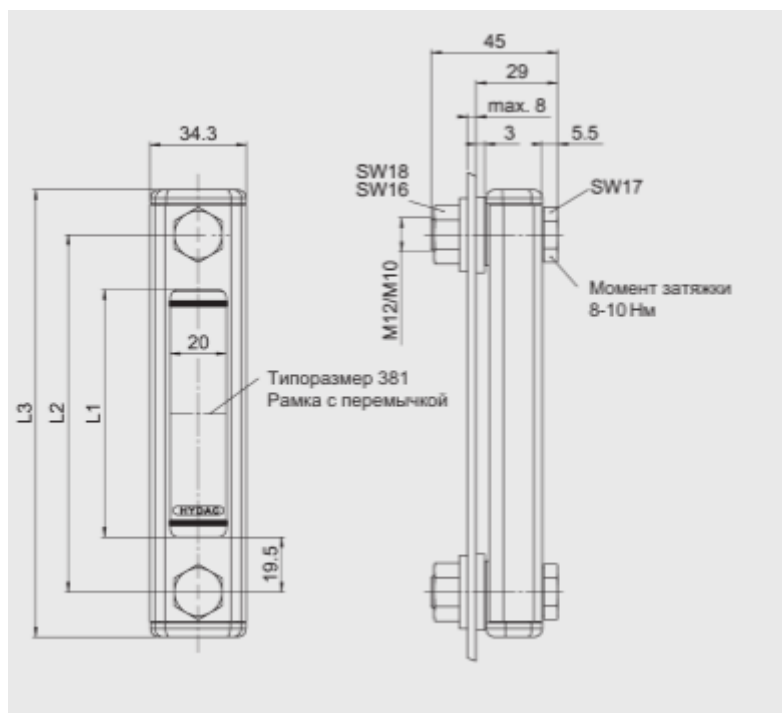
Габаритные и присоединительные размеры маслоуказателя с термометром
